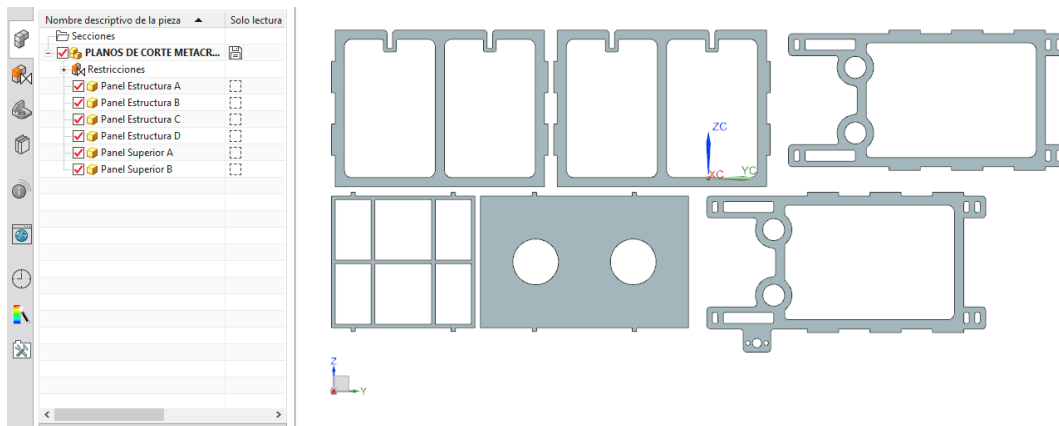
Disposición de las piezas para corte láser en metacrilato / Fuente: Propia
